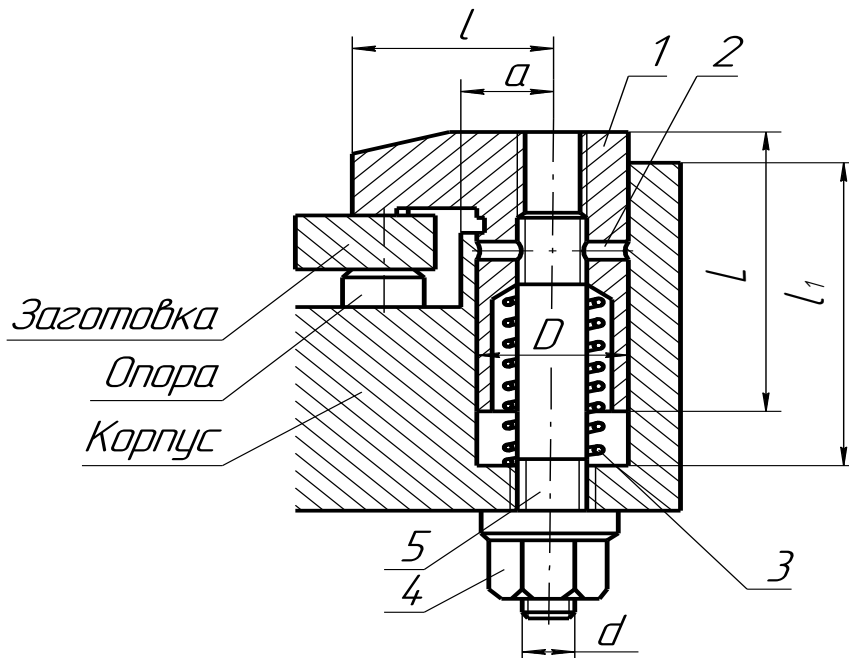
Конструкція Г- подібного комбінованого гвинтового ЗМ, що затискаються знизу. 1 - прихват Г- подібний, 2 - штифт, 3 - пружина, 4 - гайка затискна, 5 - шпилька.
